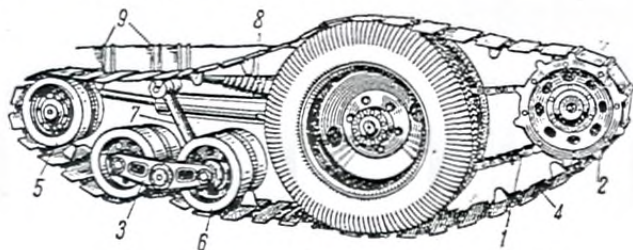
Общий вид гусеничного двигателя ЗИС-5:
